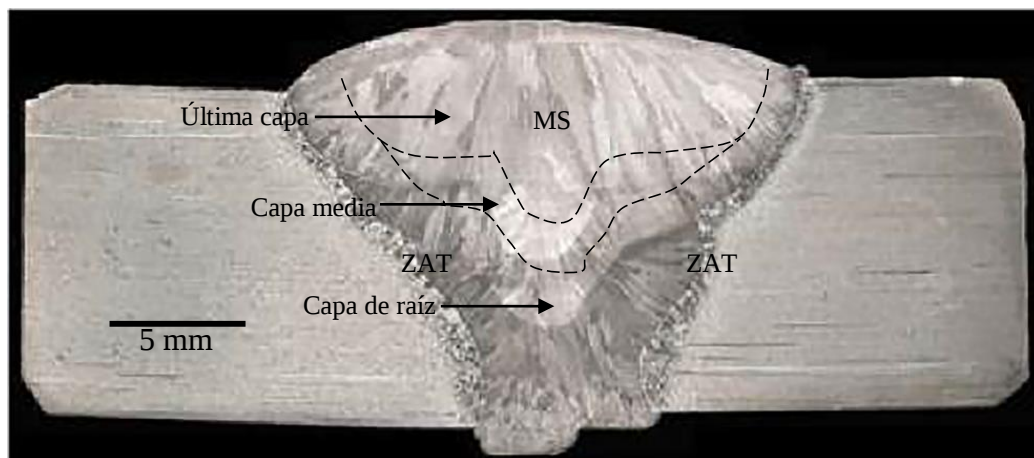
Macrografías de la junta soldada Inconel 600 [9].
